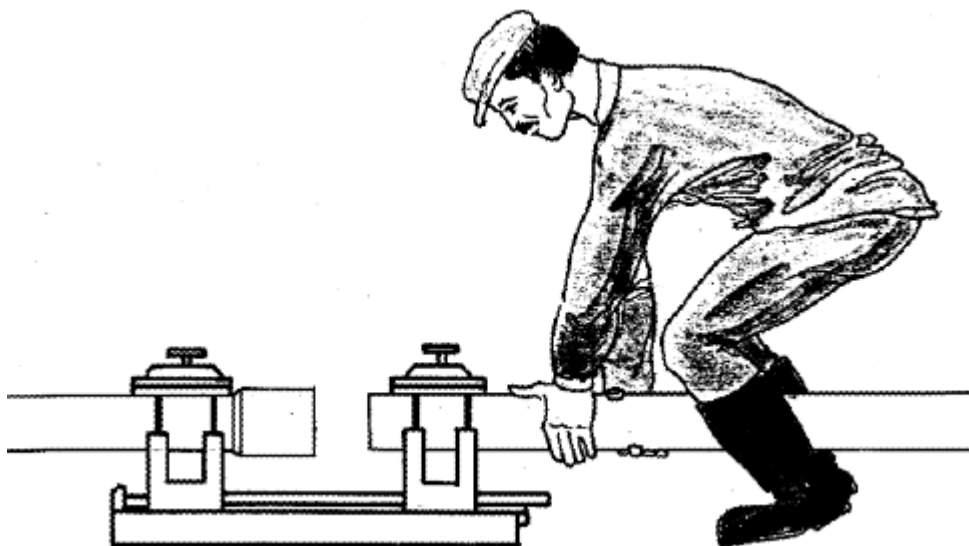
Подготовка зажимного приспособления к работе и крепление.
